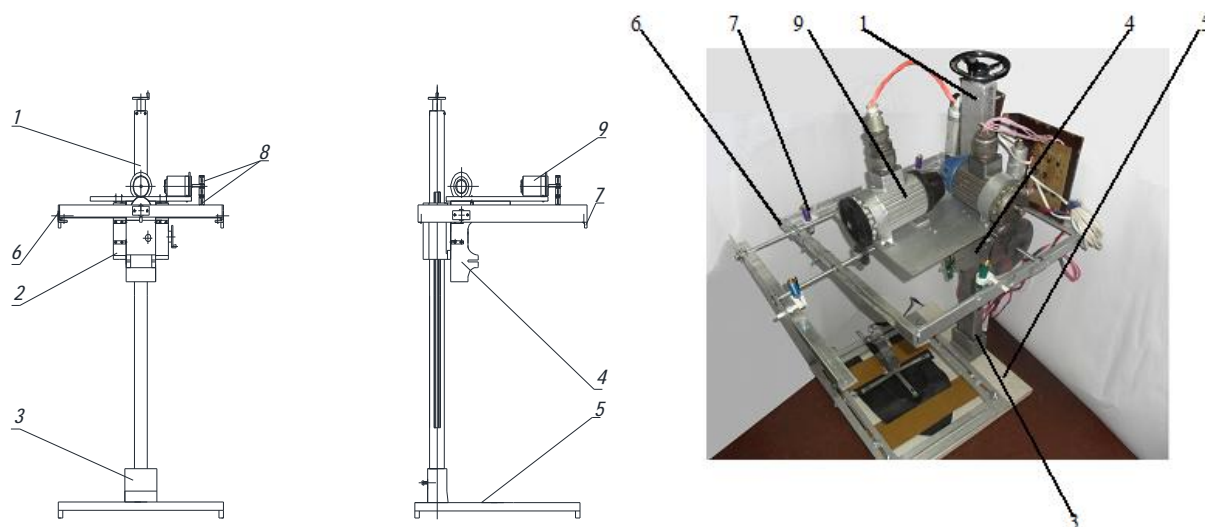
Загальний вигляд пристосування для базування деталей ЗВВ: 1 – станина; 2 – станина повзуна 3 – опора; 4 – повзун основи; 5 – плита; 6 – кутники; 7 – крокові двигуни; 8 – базуючі елементи
